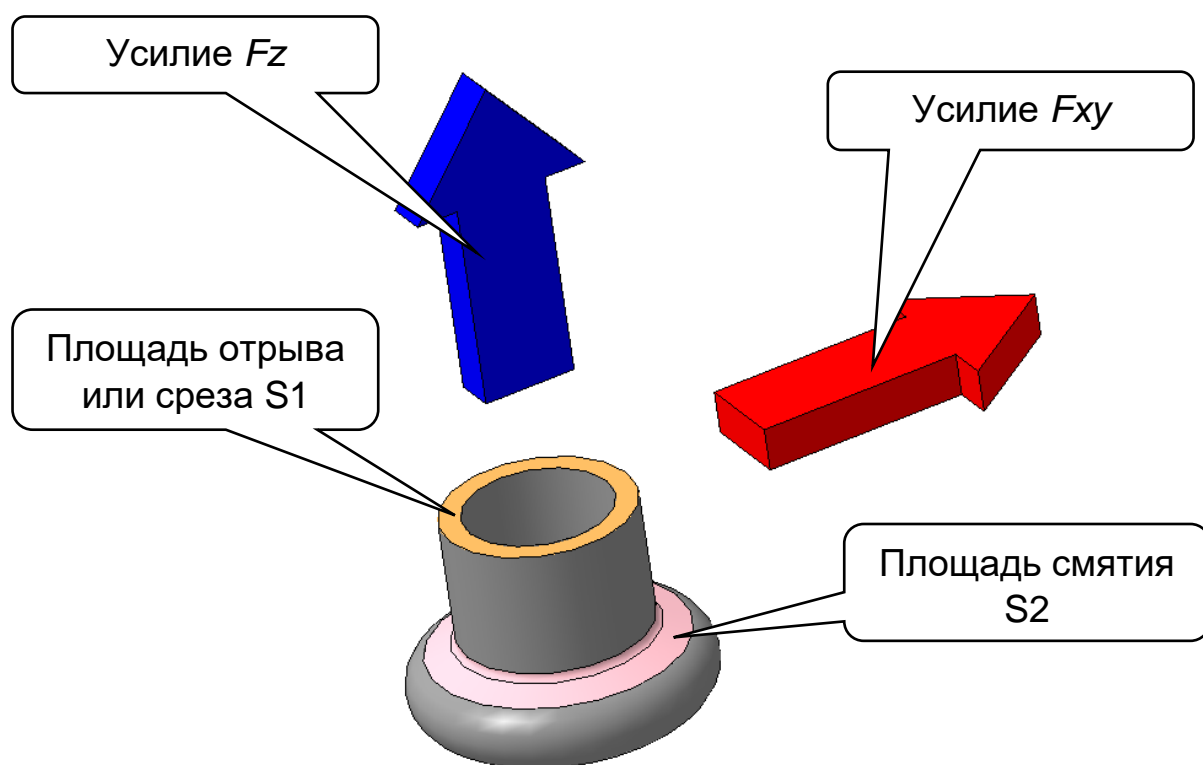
Усилия и площади стержня соединения, воспринимающие нагрузку от усилий
